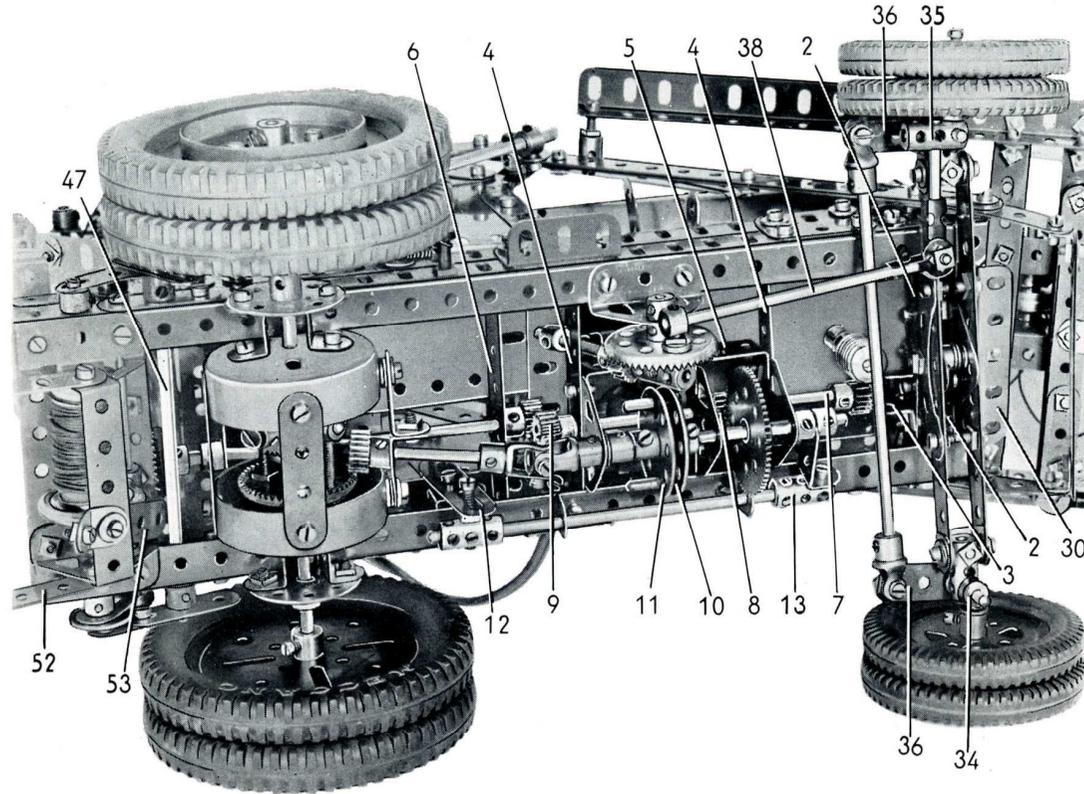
La benne automobile vue de dessous, on aperçoit clairement le train d'engrenages et le mécanisme.
